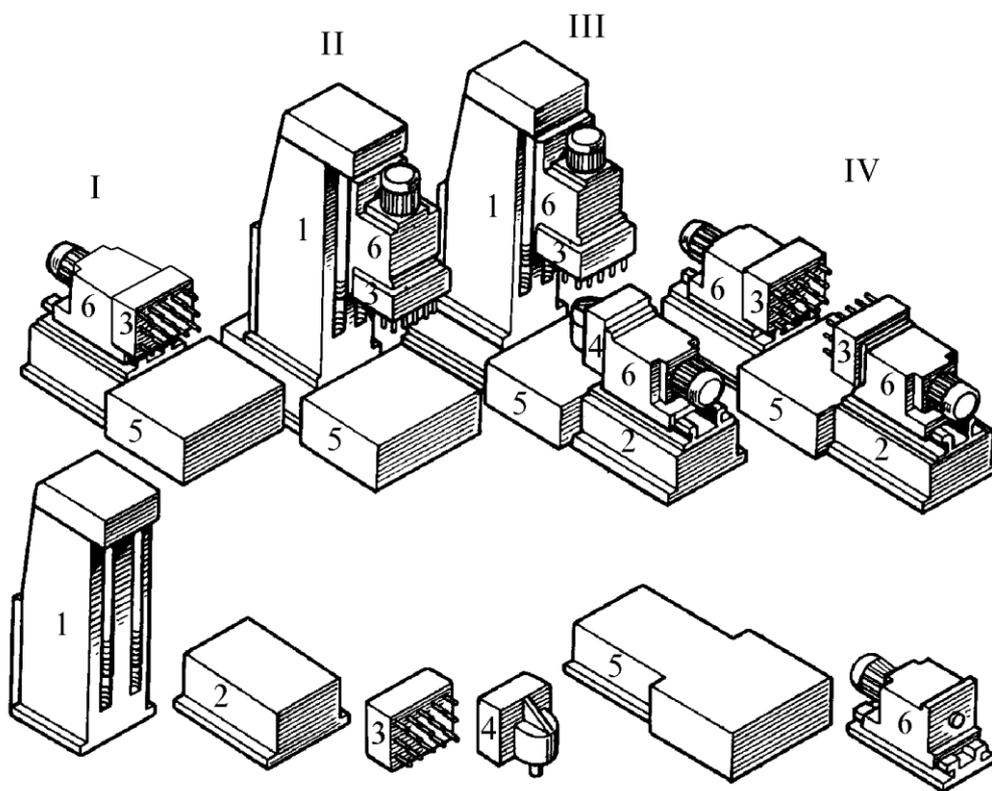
Схема компоновки многопозиционных агрегатных станков:
